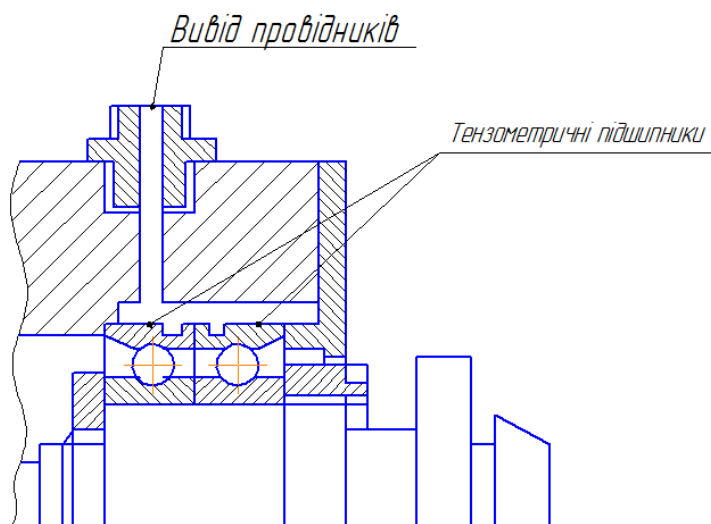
Передня опора шпинделя верстату з тензометричними підшипниками
